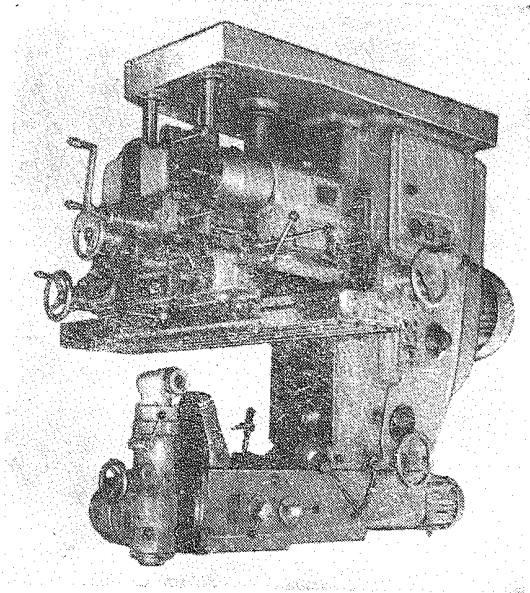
а. Широкоуниверсальный консольно-фрезерный станок модели 6М83П
